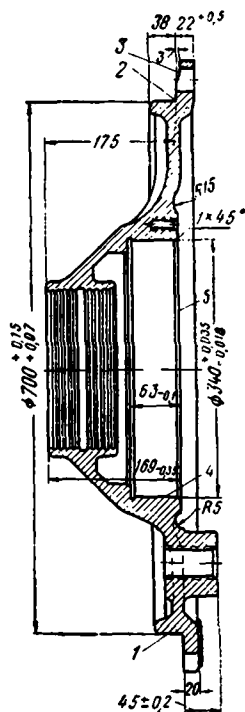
Последовательность операций токарной обработки подшипникового щита двигателя НБ-411
